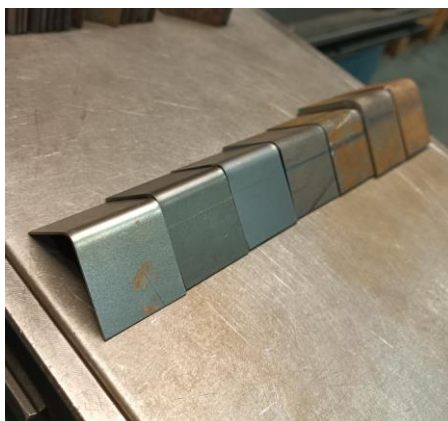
Место контакта заготовок из Ст3 и 08пс с матрицей
